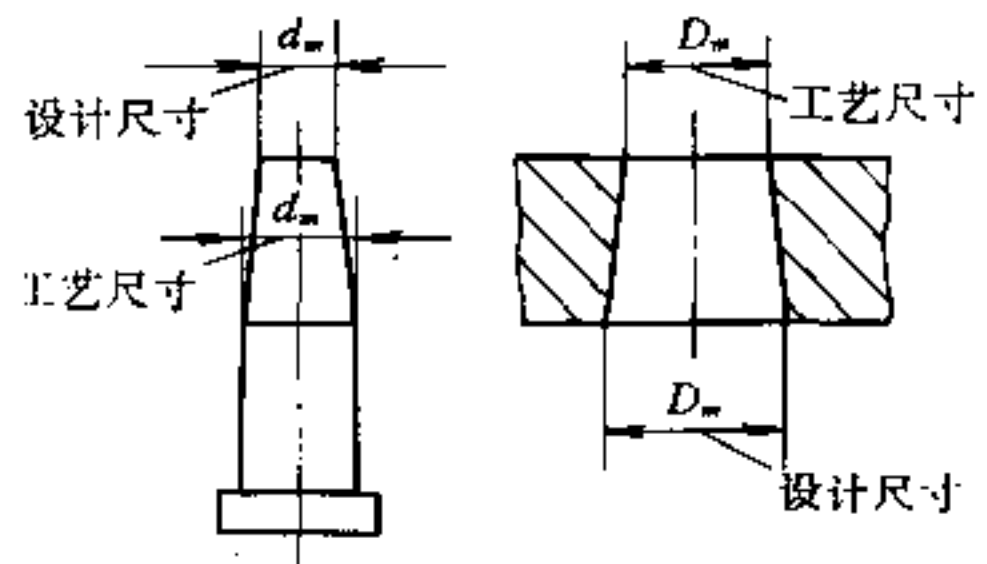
脱模斜度对成型零件尺寸及公差标注要求
